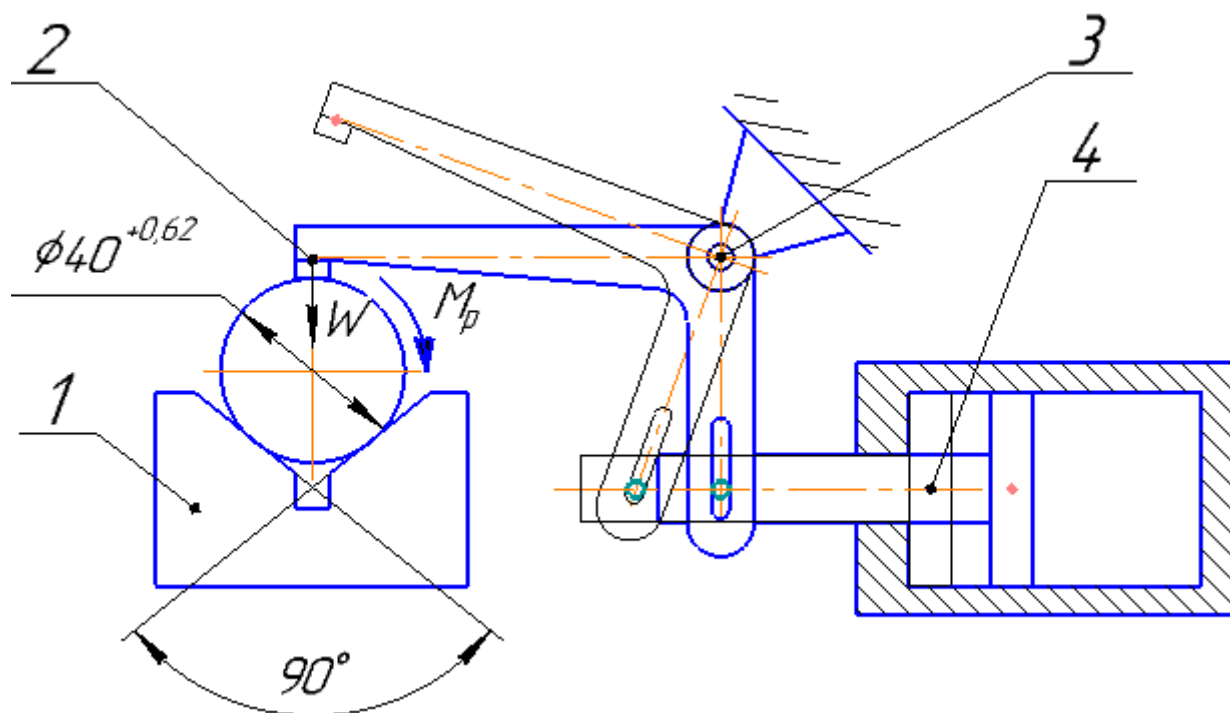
Кинематическая схема гидравлического зажима: 1 – Призма; 2 – рычаг; 3 – ось; 4 – гидроцилиндр; Д – деталь.
